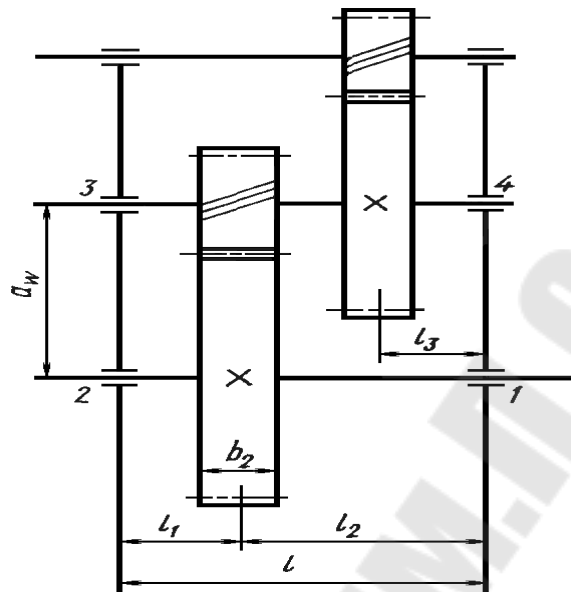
Схема к расчету допуска расстояния между осями корпуса
